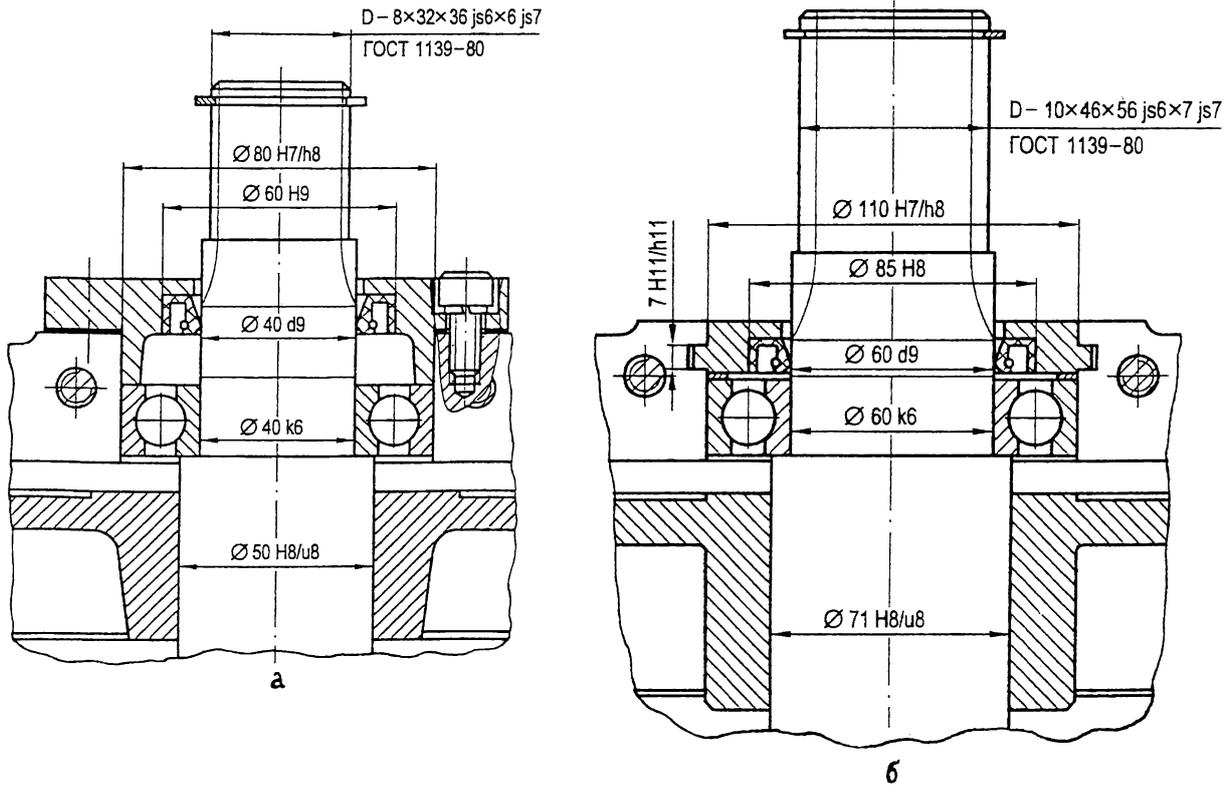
Примеры конструкций подшипниковых узлов с привёртными (а) и закладными (б) крышками подшипников
